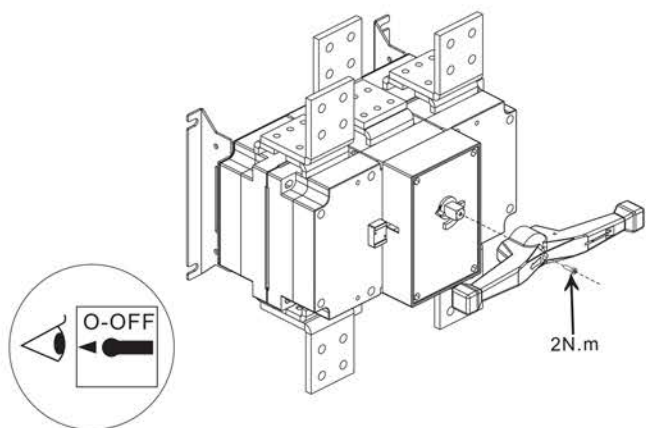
а – Монтаж ручки на корпус рубильников 2000-4000 А
